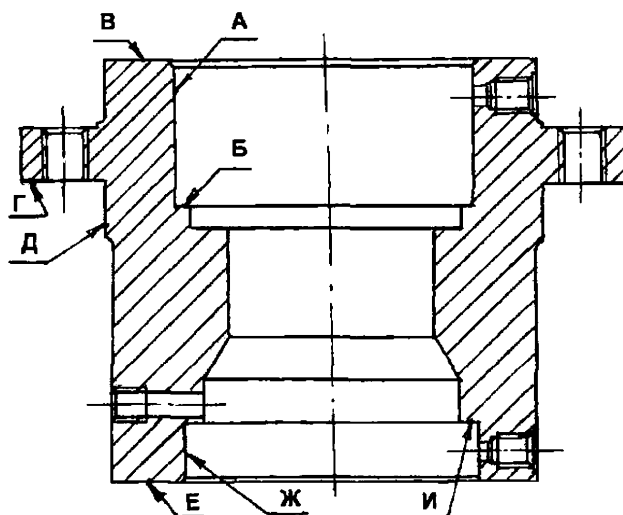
Корпус подшипника (поз. 7, рисунок 55)
